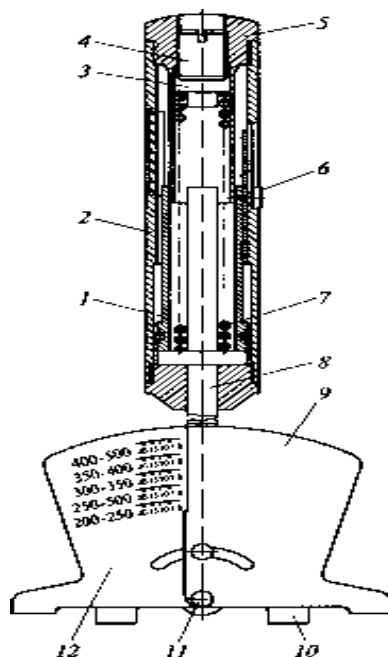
Приспособление мод. КИ-8920 для проверки натяжения ремней:
